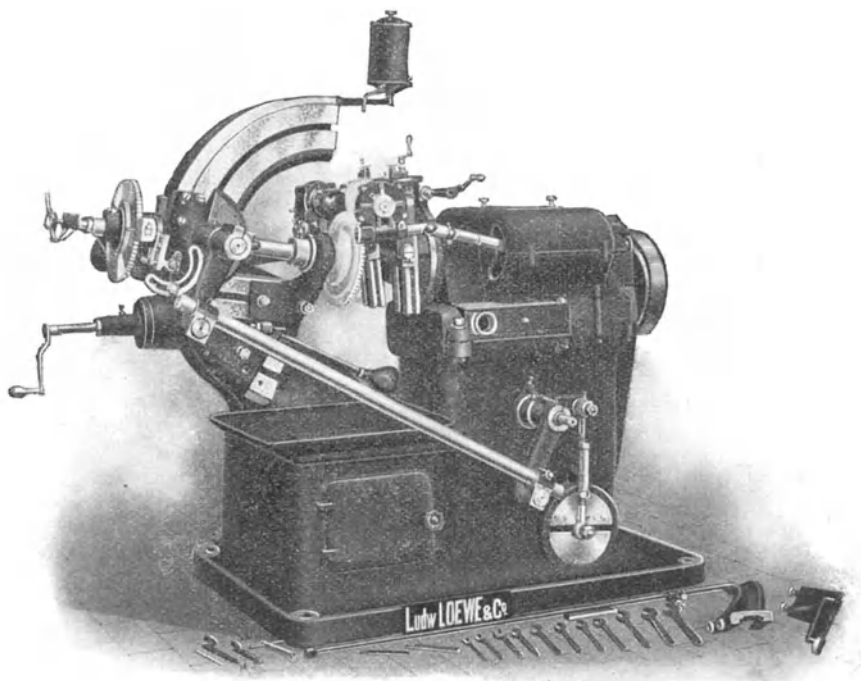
Die automatische Kegelhäderfräsmaschine von L. Löwe & Co.
